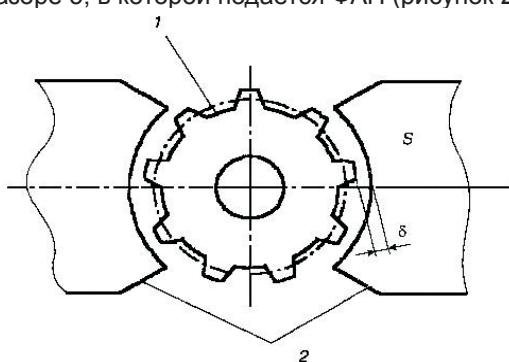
Схема магнитно-абразивной обработки зубчатых колес.
